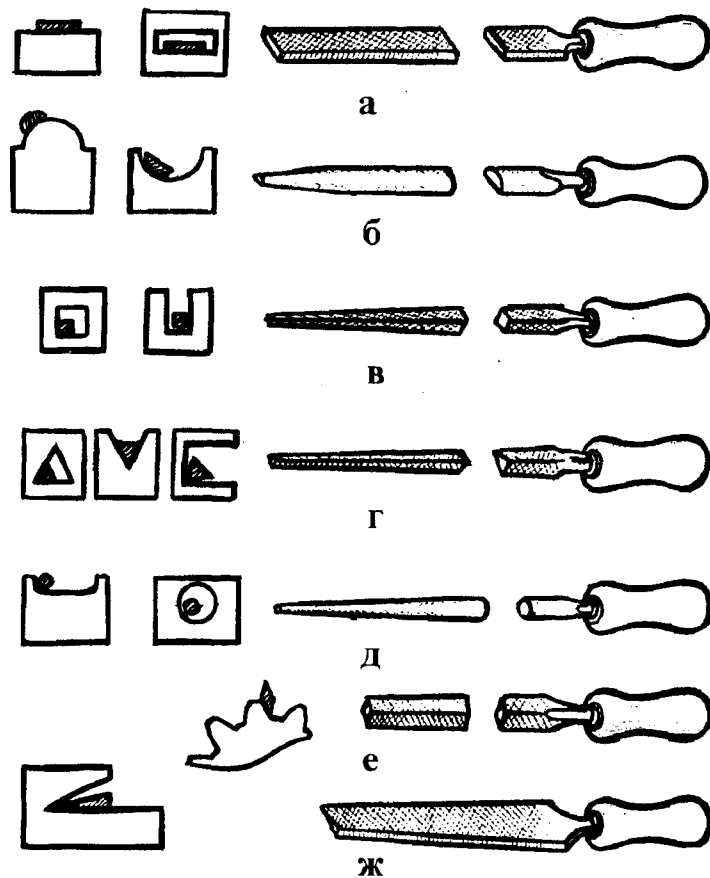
Виды напильников: а — плоский; б — полукруглый; в — квадратный; г — трехгранный; д — круглый; е — ромбический; ж — ножевой
